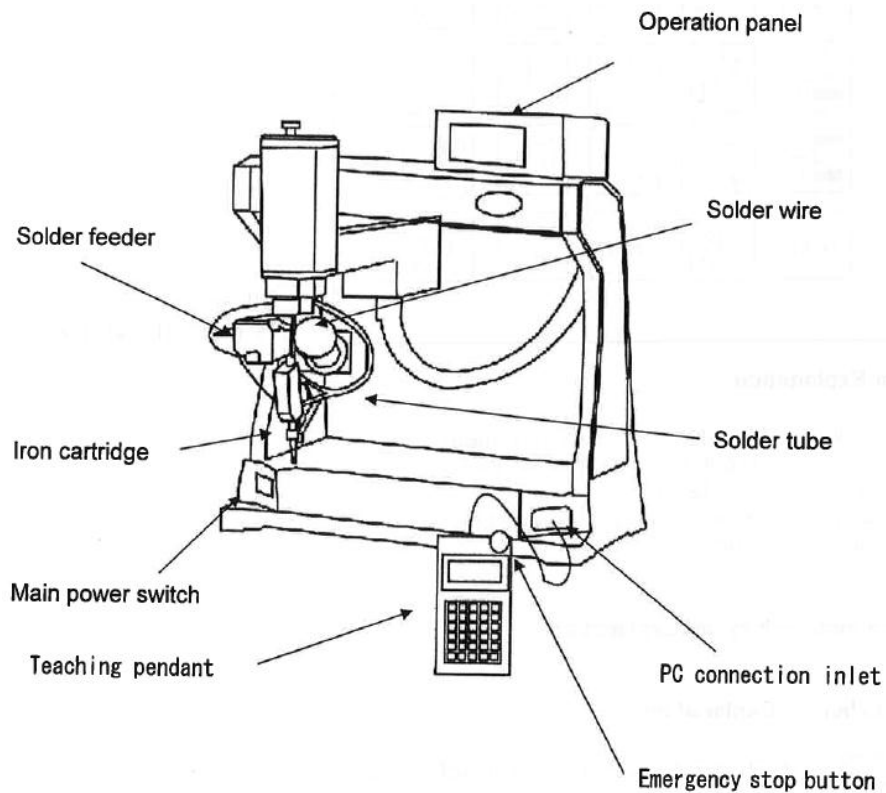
Descripción de partes de Robot Soldador
